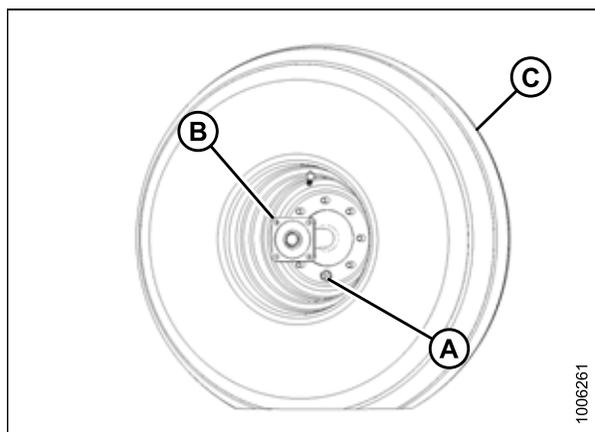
Вилочное самоустанавливающееся колесо
